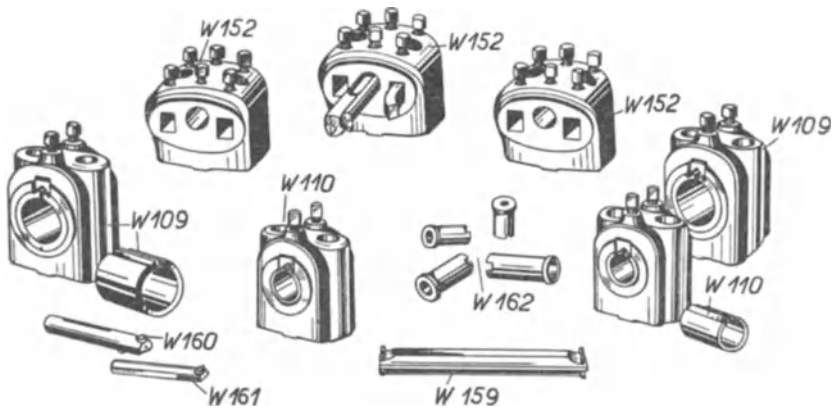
Futterwerkzeuge für Tischrevolvertänke.
